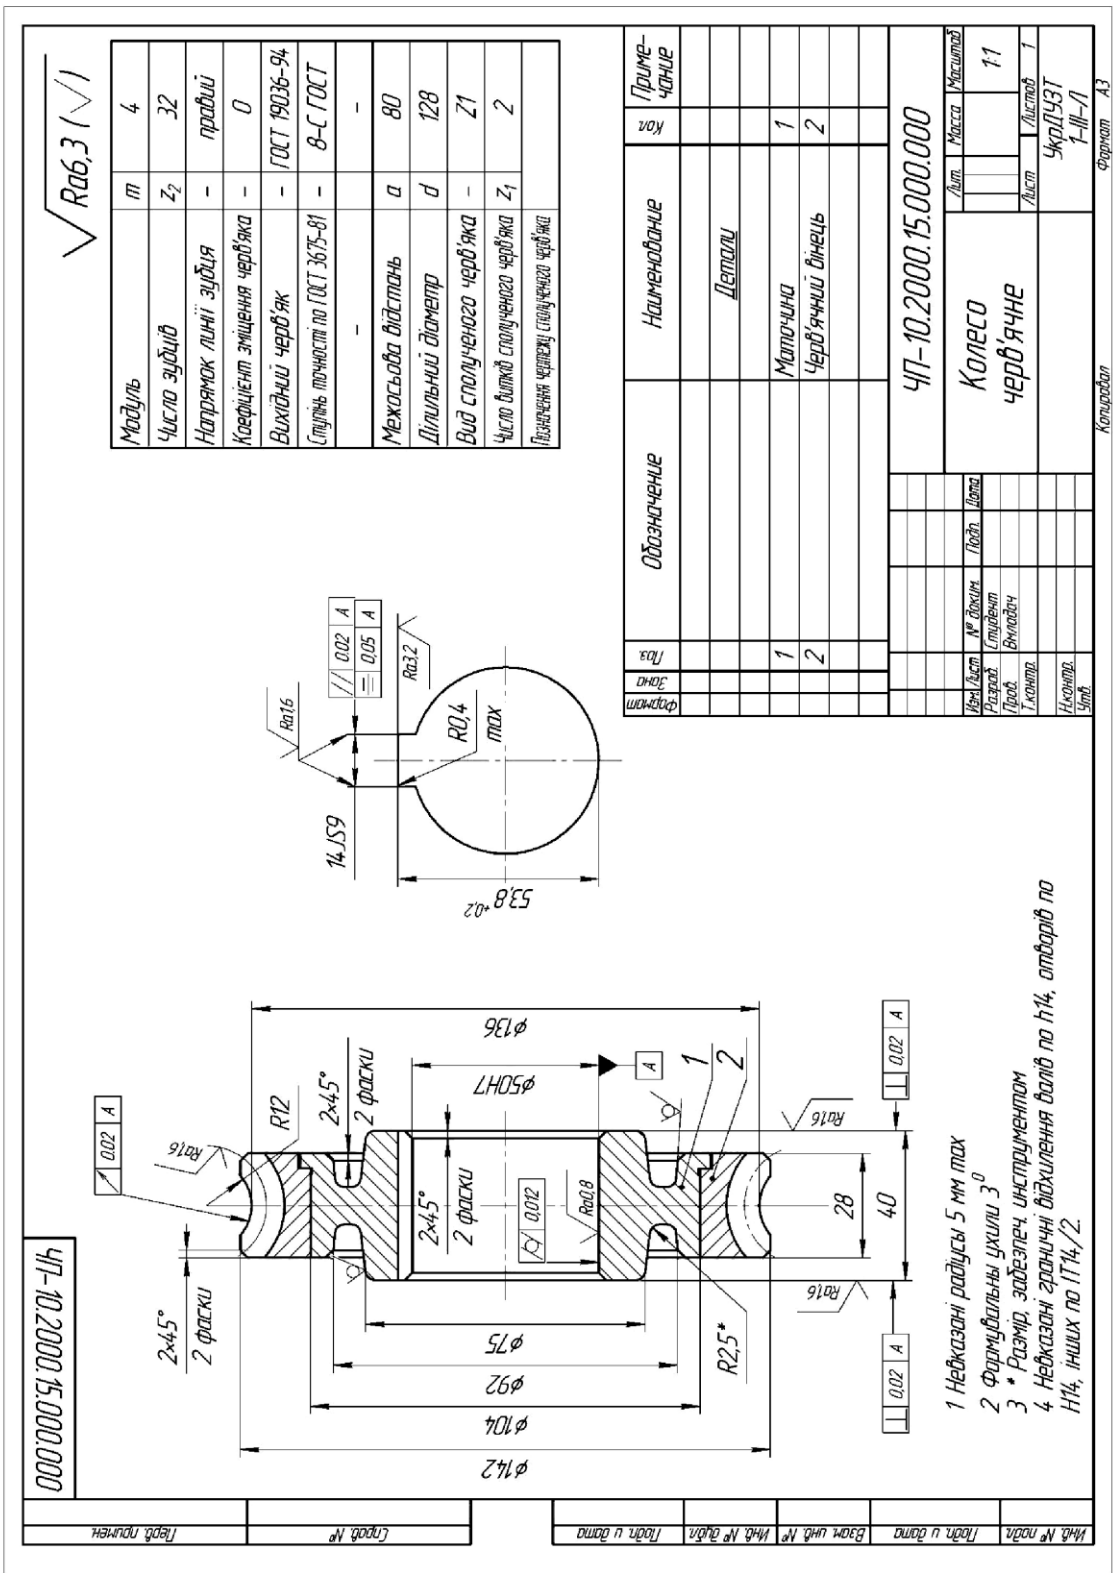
Робоче креслення черв'ячного колеса
